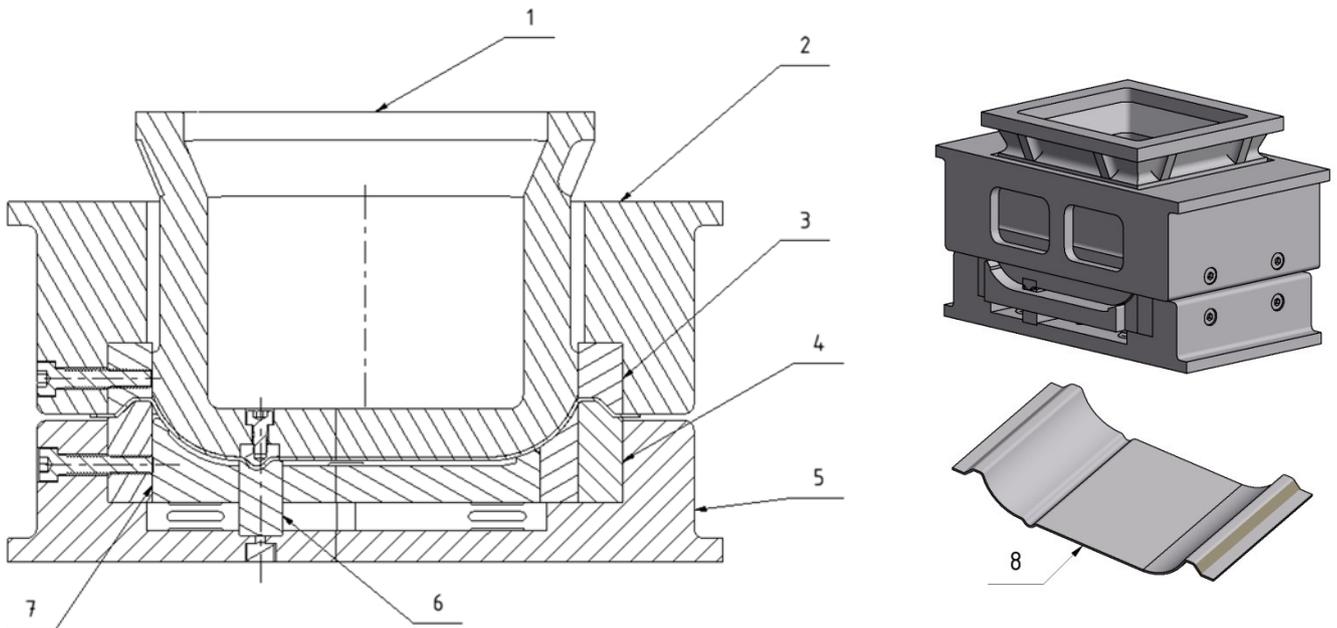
Beschneidewerkzeug für Tiefziehform
